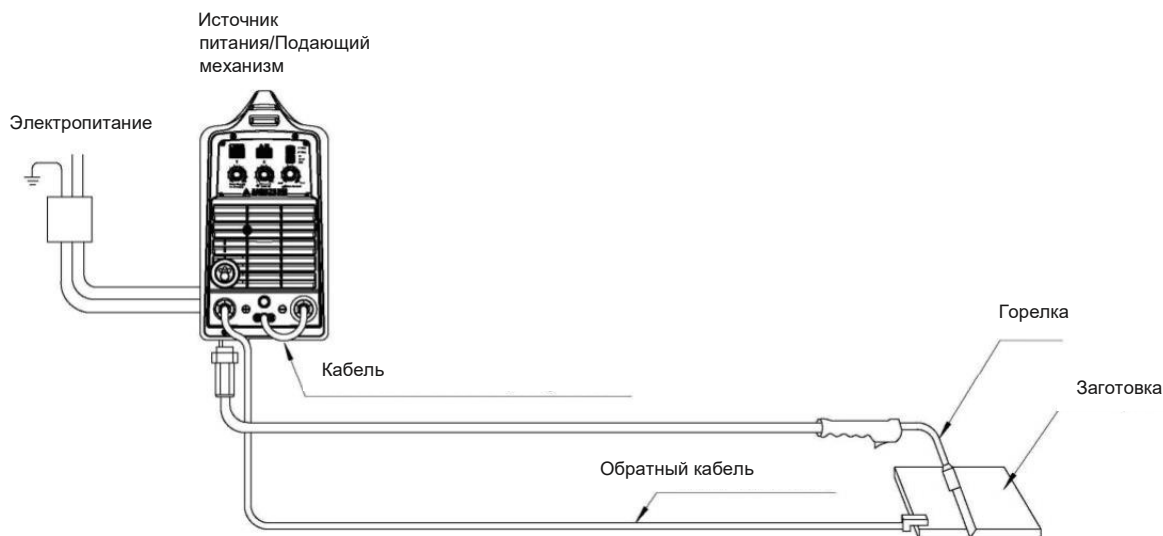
Сварка порошковой проволокой FCAW-S с помощью горелки типа «толкатель проволоки»
